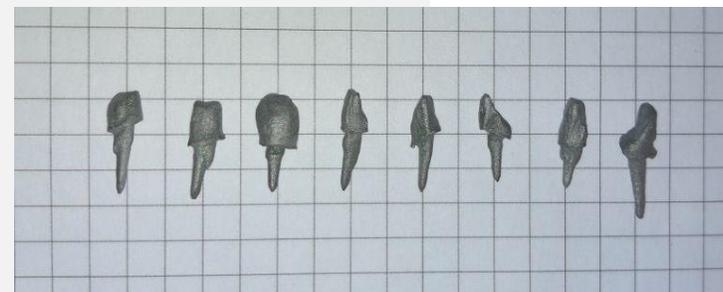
Вкладки отлитые по напечатанным заготовкам
